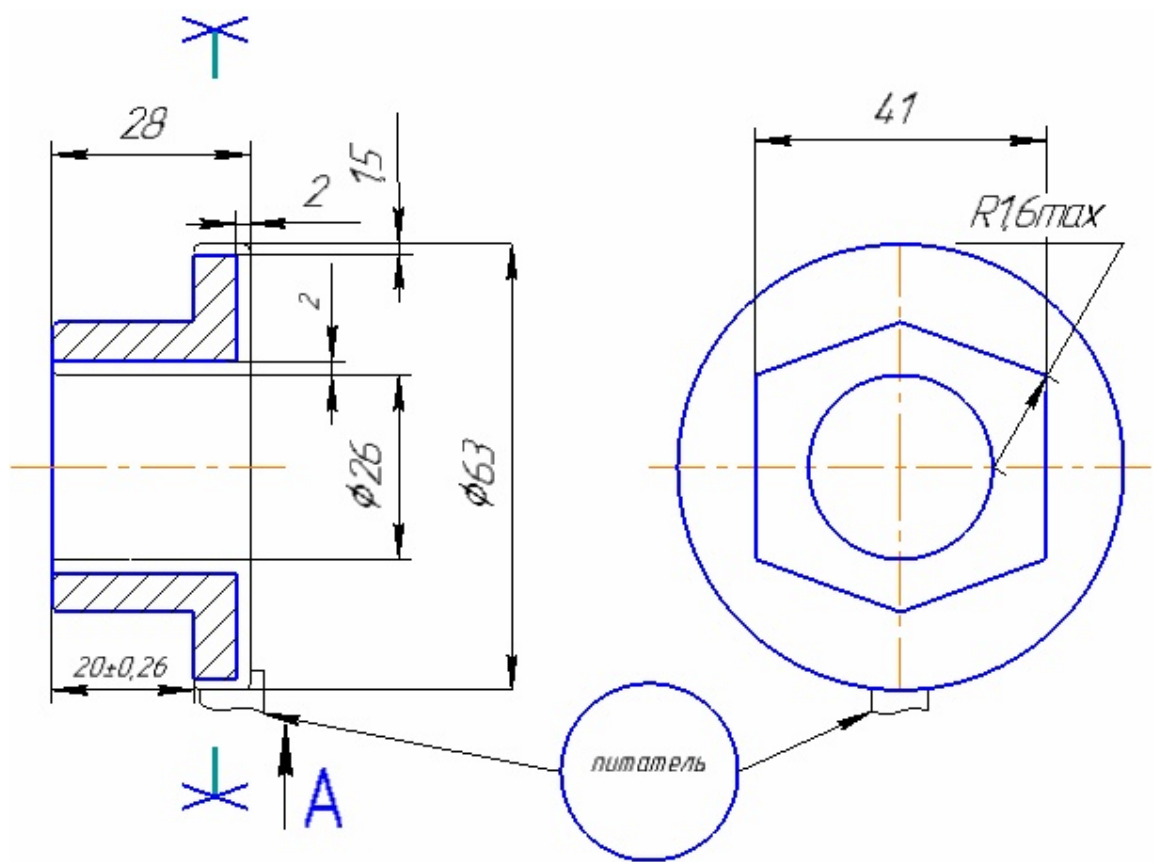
Эскиз отливки с поверхностью разреза пресс-формы.
